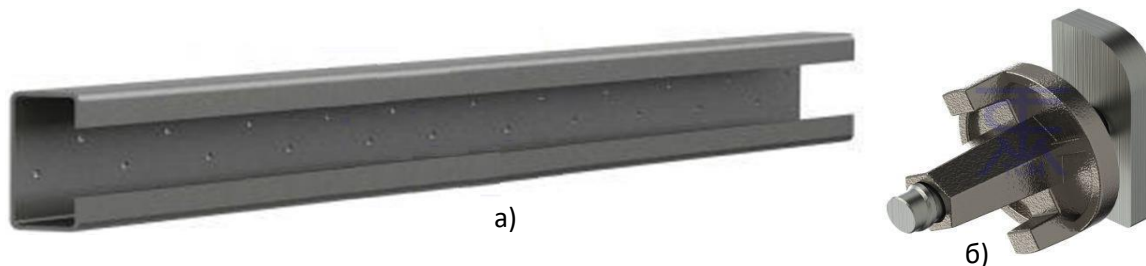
Деталі кріплення кронштейнів: а – C-профіль; б – кріпильний болт
